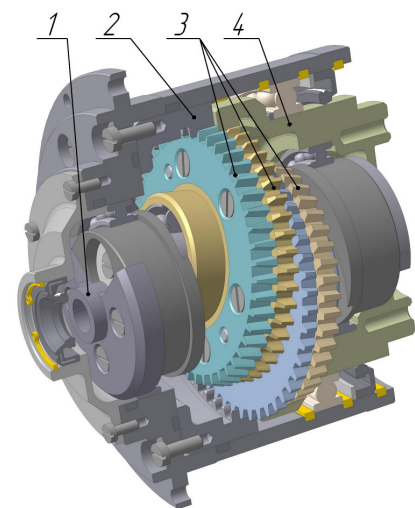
Планетарный редуктор с цилиндро-коническими зацеплениями:
